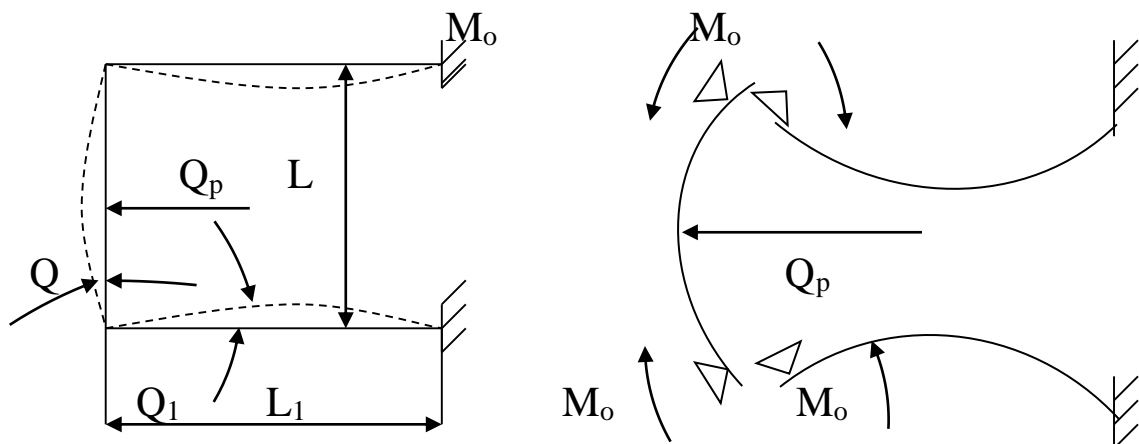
Розрахункова схема станини щоккової дробарки
